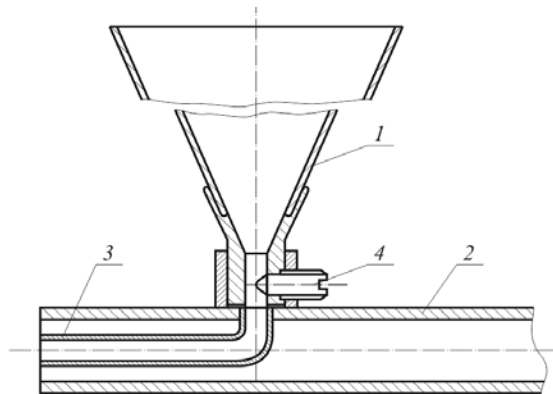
Схема сопла металізатора для створення комбінованого повітряно-порошкового розпилювального струменя:
